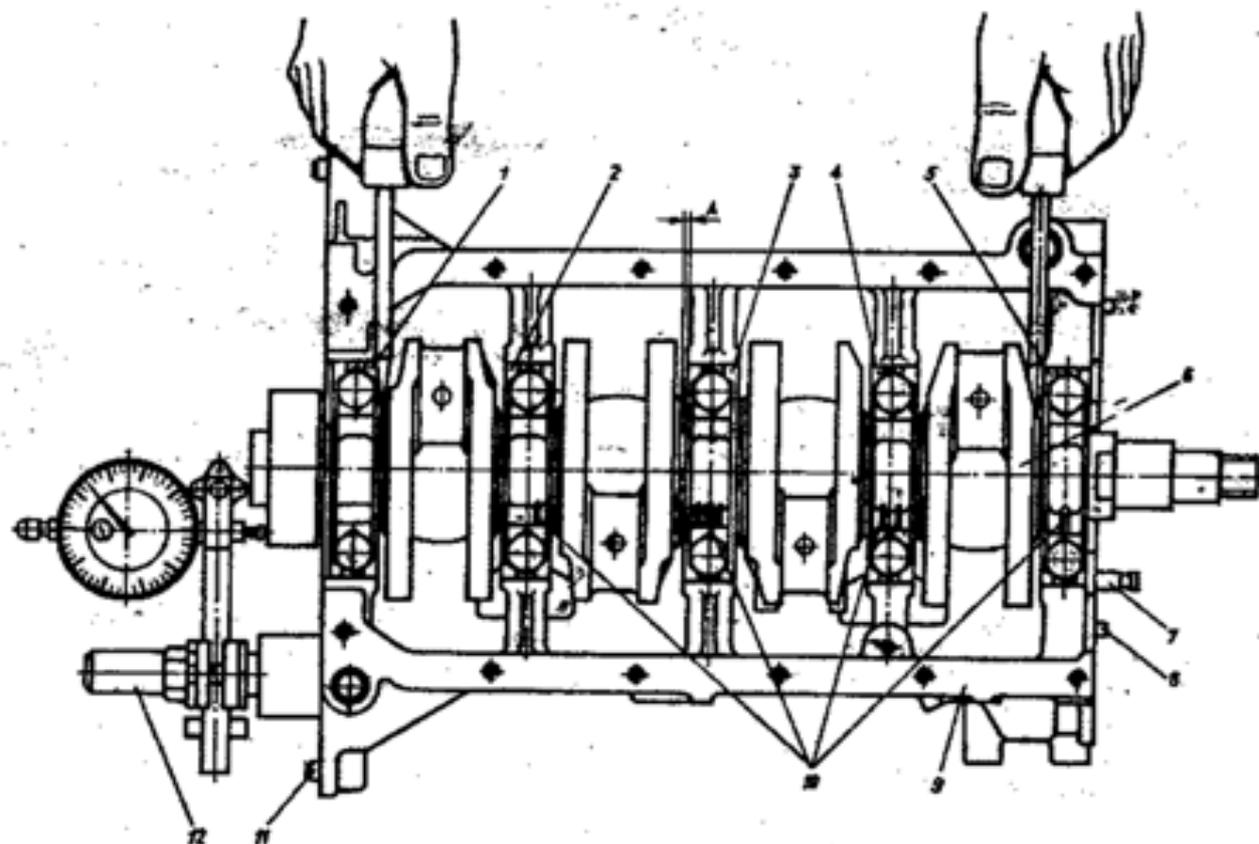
Проверка осевого разбега и маркировки крышек подшипников коленчатого вала: 1, 2, 4, 5-крышки подшипников; 3-средняя крышка подшипника; 6-коленчатый вал; 7-упор пружины натяжителя; 8-штифт установочный; 9-блок цилиндров; 10-метки крышек подшипников; 11-штула установочная; 12-магнитная стойка с индикатором; А-осевой разбег 0,054...0,306 мм
